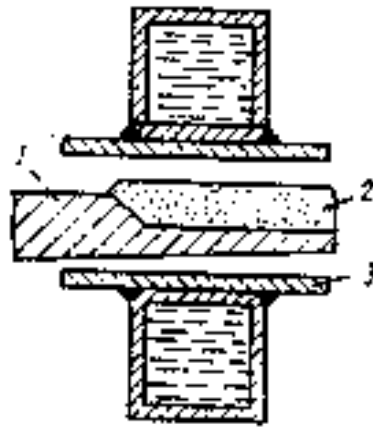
Наплавлення твердим присадочним матеріалом: 1- деталь, 2 - суміш порошків сплава і флюса, 3 – індуктор
